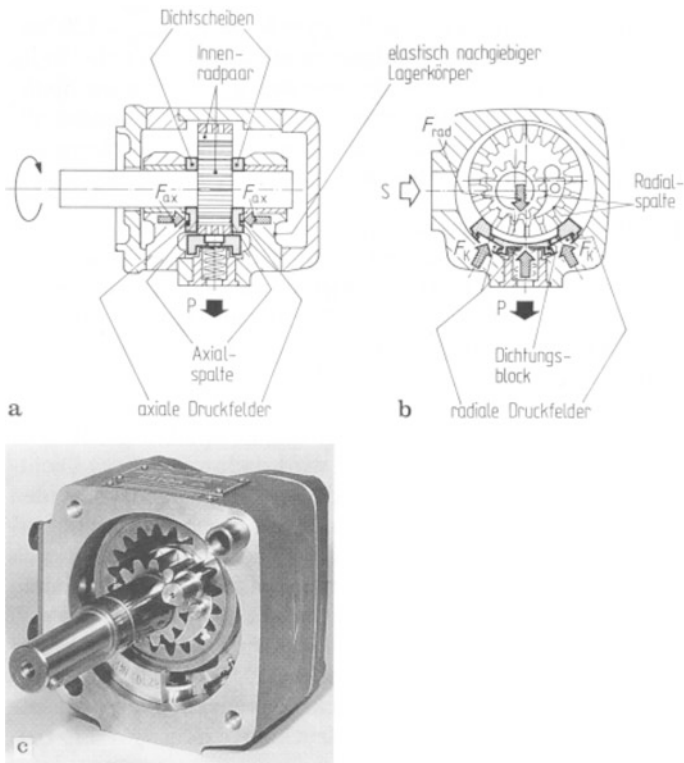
Innenzahradpumpe mit hydraulischem Spaltausgleich, vollständig druckkompensiert (IPH, Eckerle und Voith). a Axiale Druckkompensation mittels Dichtelemente Axialseiben; b radiale (aktive) Druckkompensation mittels Dichtelement Steuerkolben; c Schnittmodell
